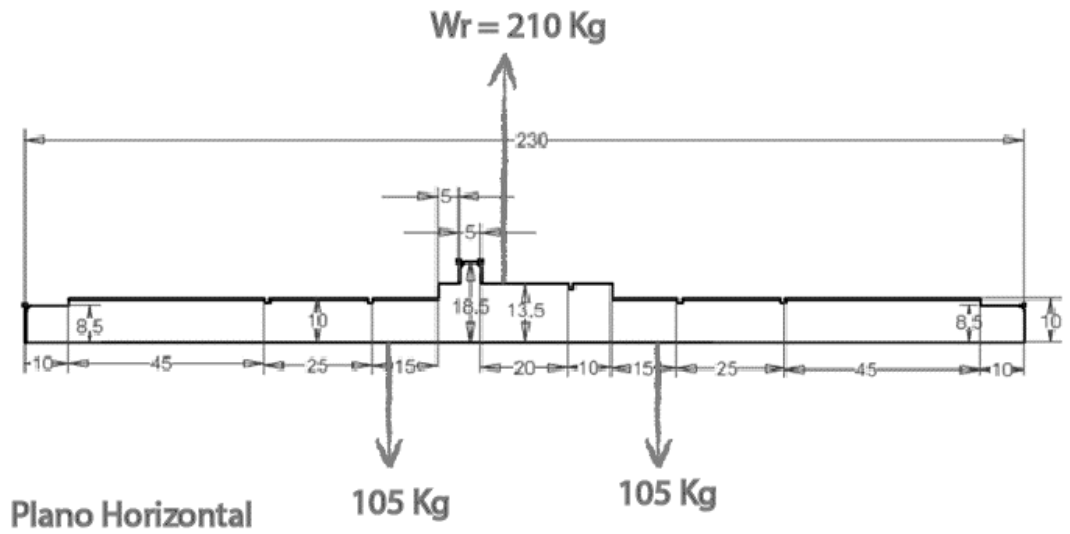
Fuerza en el eje de carrete en el plano horizontal. Fuente. – Elaboración propia.
